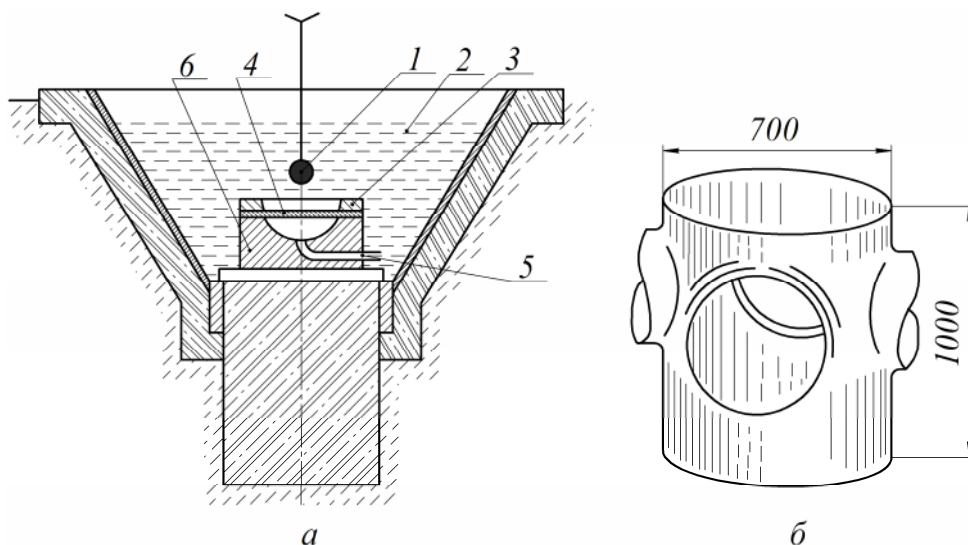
Установка для штампування вибухом (*a*) і деталь (*б*), одержана цим способом
